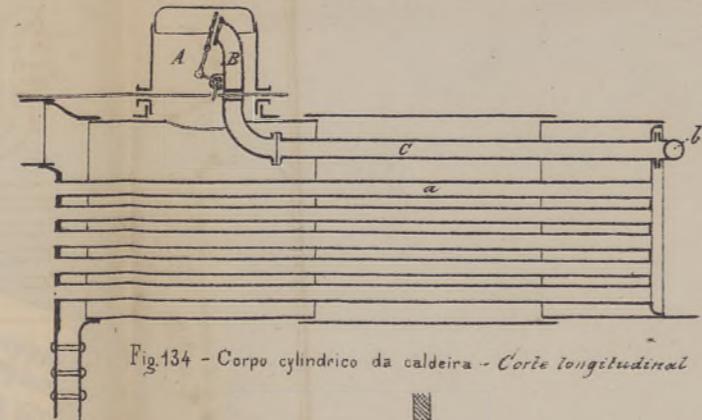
Corpo cylindrico da caldeira - Corte longitudinal
